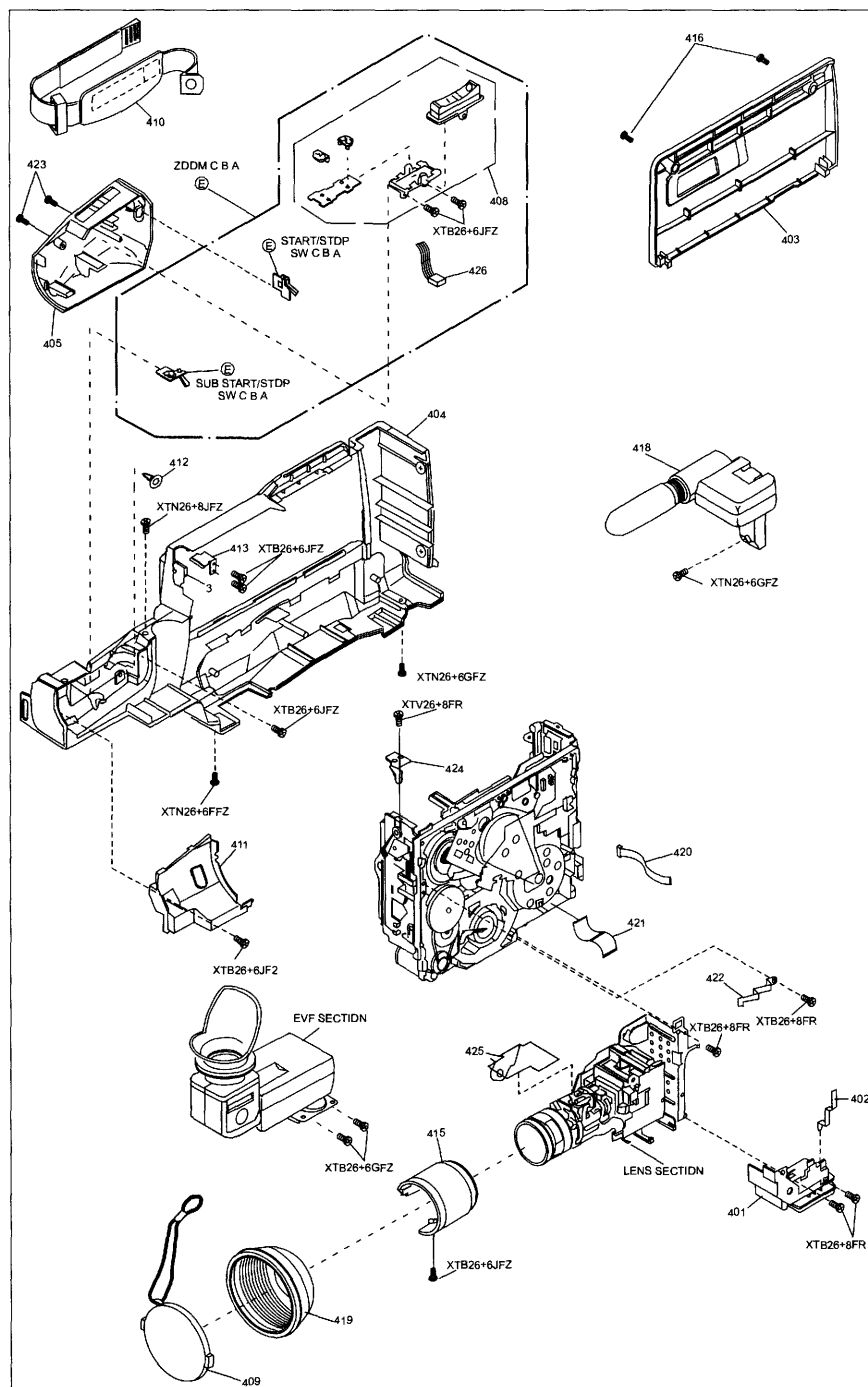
Сборочный чертеж корпуса видеокамер «Panasonic NV-MS4E/B/A, M9000EN/MC» (вид справа)
